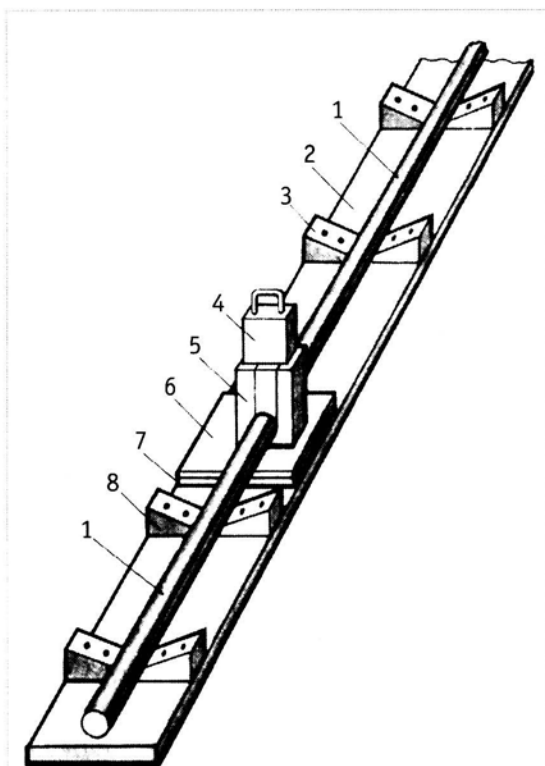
Устройство для тепловой обработки пластмассовых труб при сварке встык: 1 — труба; 2 — деревянная доска; 3 — гвоздь; 4 — нагревательное приспособление; 5 — металлический лист; 6 — асбестовый лист; 7 — металлический лист; 8 — деревянная направляющая
